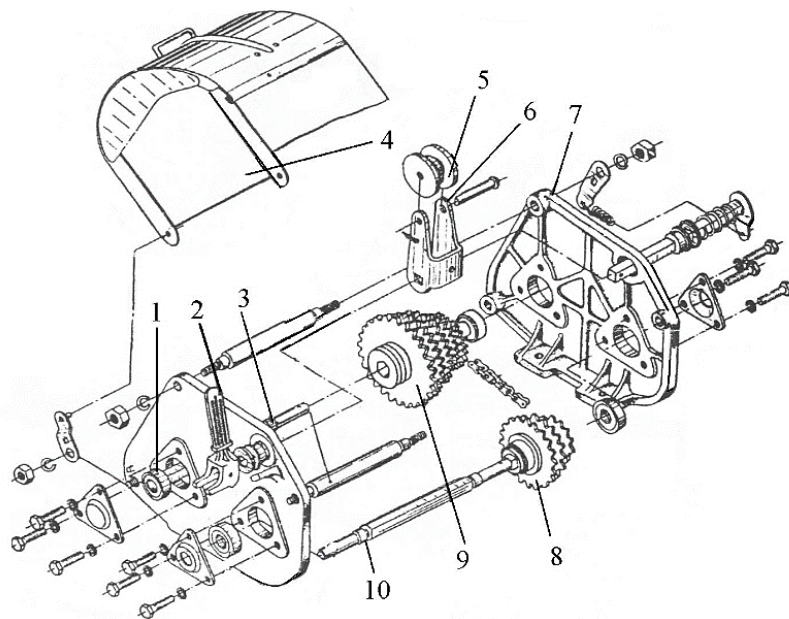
Редуктор механізму приводу насінневого висівного апарата сівалки типу СУПН:
